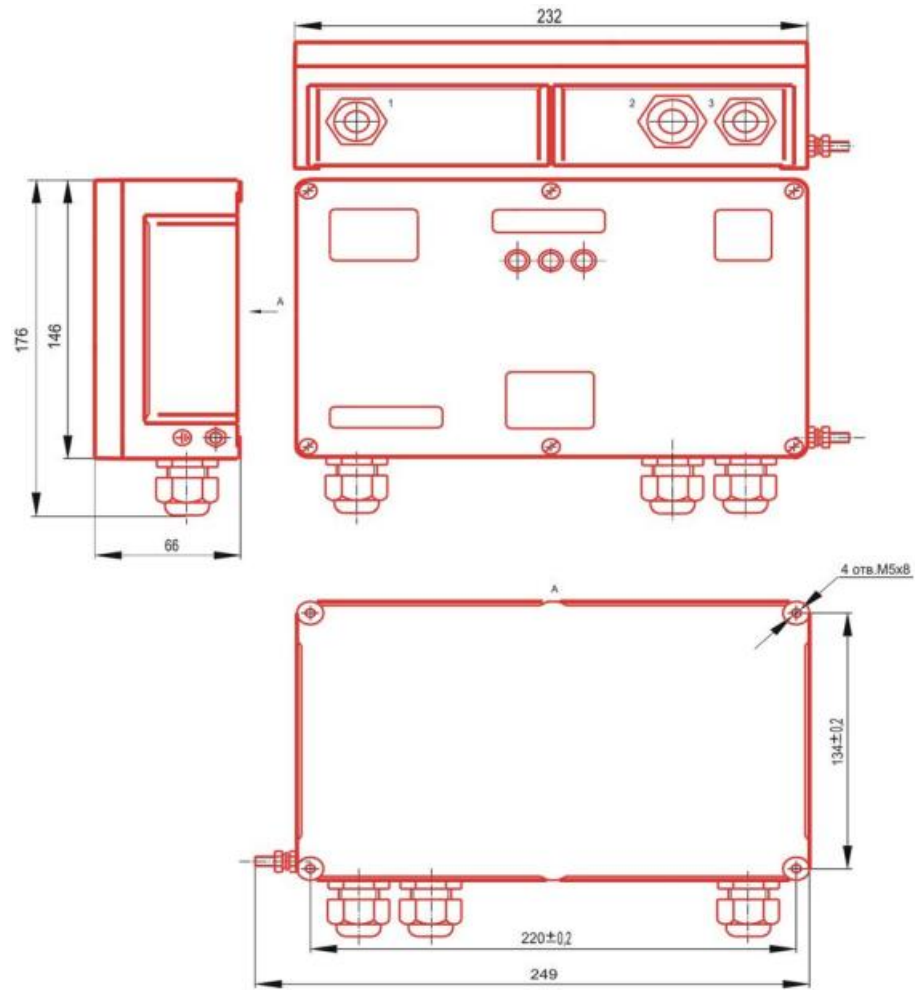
Внешний вид и габаритные размеры датчика ET77AI
